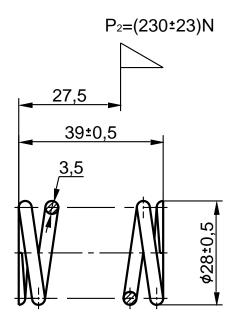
Пружина тормоза для механизма МЭО-1600
